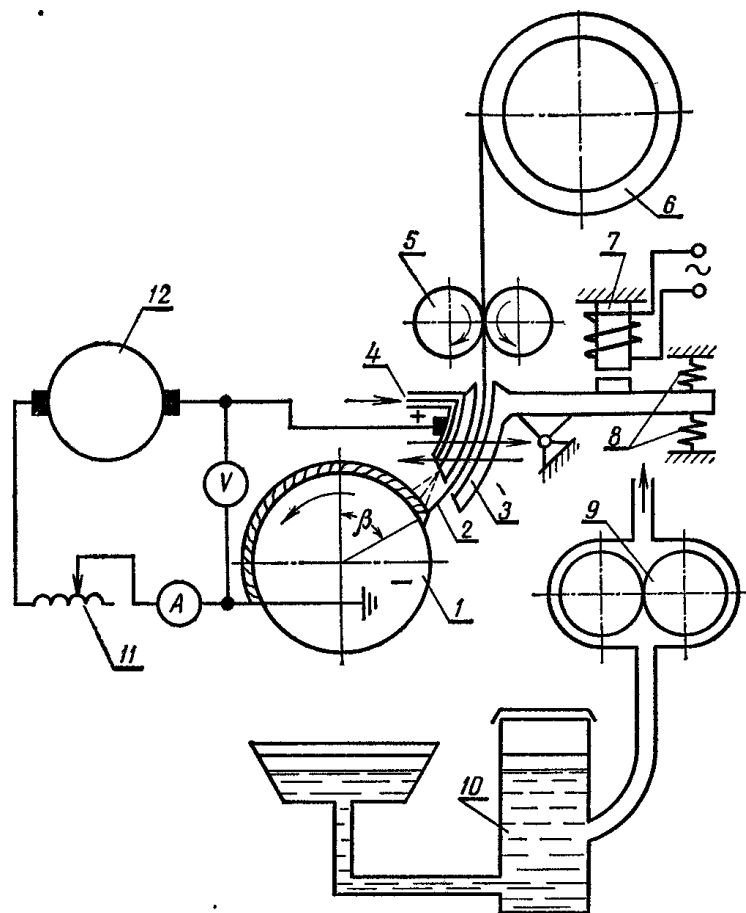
Схема установки для автоматичного вібродугового напавлення: 1 – деталь для напавлення; 2 – електрод; 3 – вібруючий мундштук, 4 – канал для подачі охолодної рідини; 5 – ролик механізму подачі; 6 – касета для дроту, 7 – вібратор; 8 – пружини; 9 – насос; 10 – фільтр-відстійник; 11 – дросель; 12 – генератор
